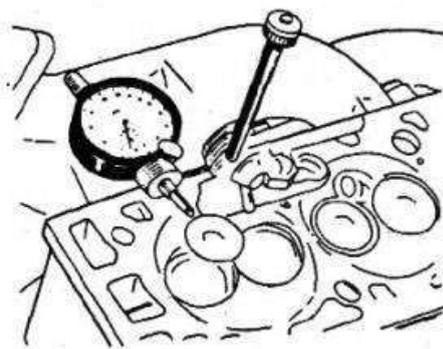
Измерение зазора между стержнем клапана и направляющей втулкой при снятой головке блока цилиндров
